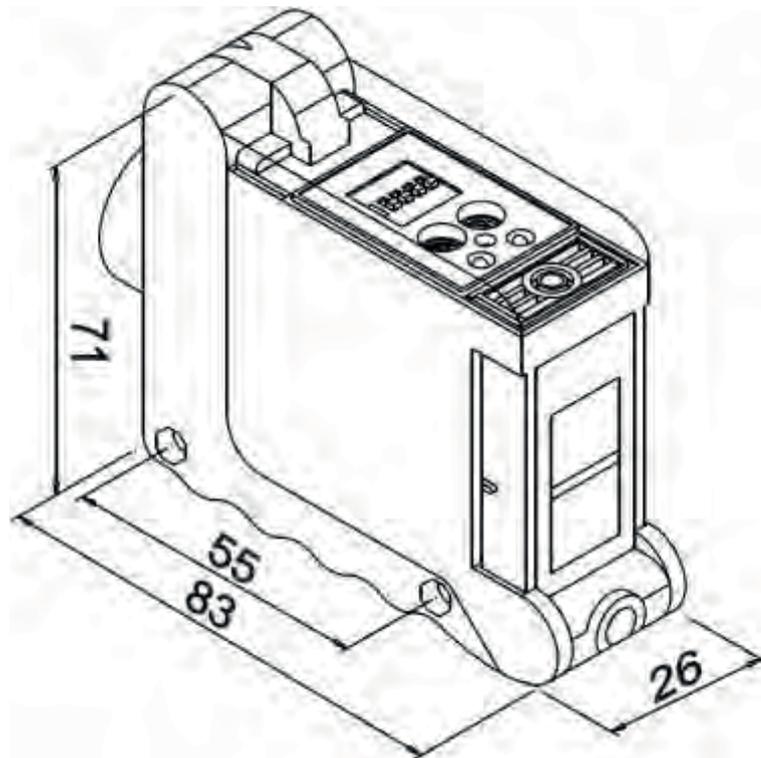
DIMENSÕES DO SENSOR (MM)
